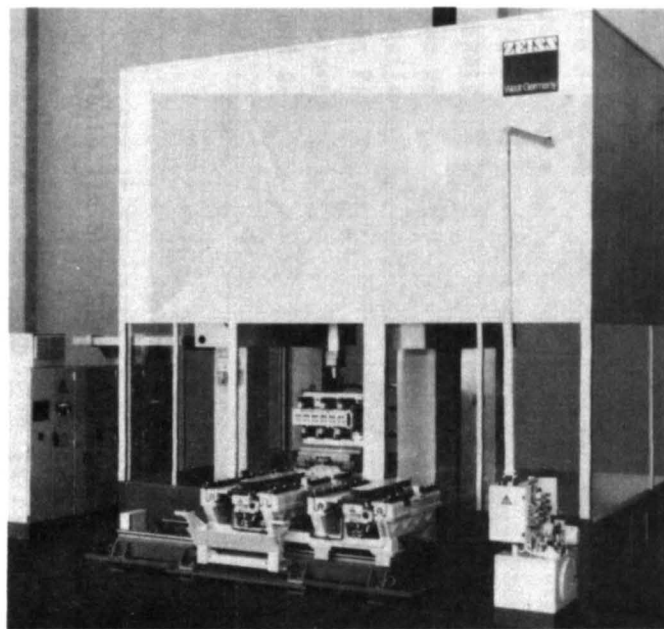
Gekapselte Portalmeßmaschine mit einem Bringe- und einem Holeplatz
